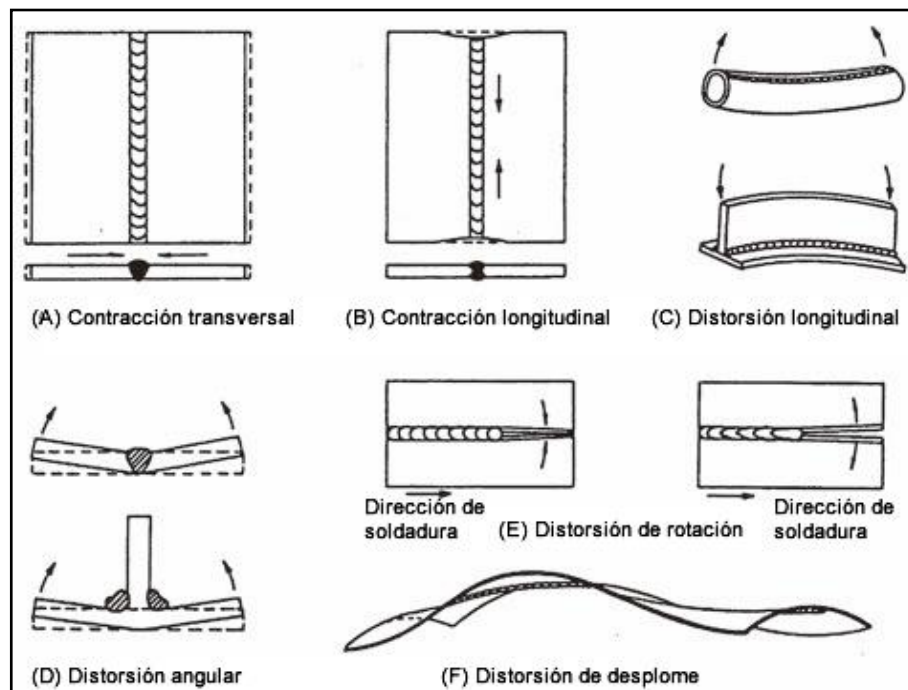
Clasificación de las formas básicas de distorsiones por soldadura (7).
